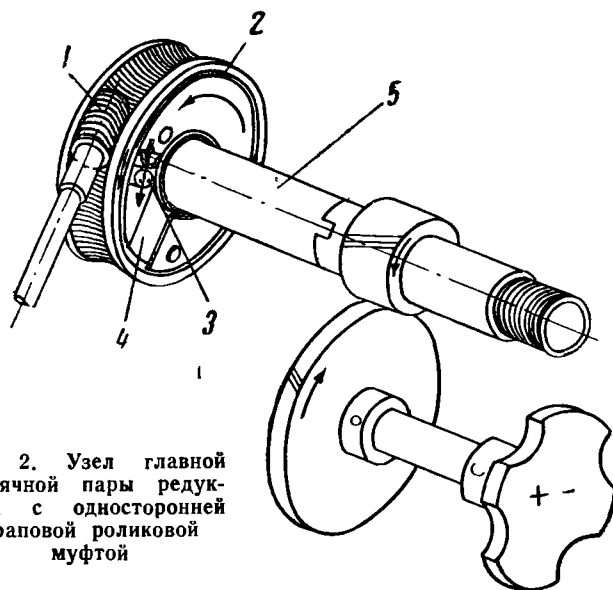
Узел главной червячной пары редуктора с односторонней храповой роликовой муфтой
